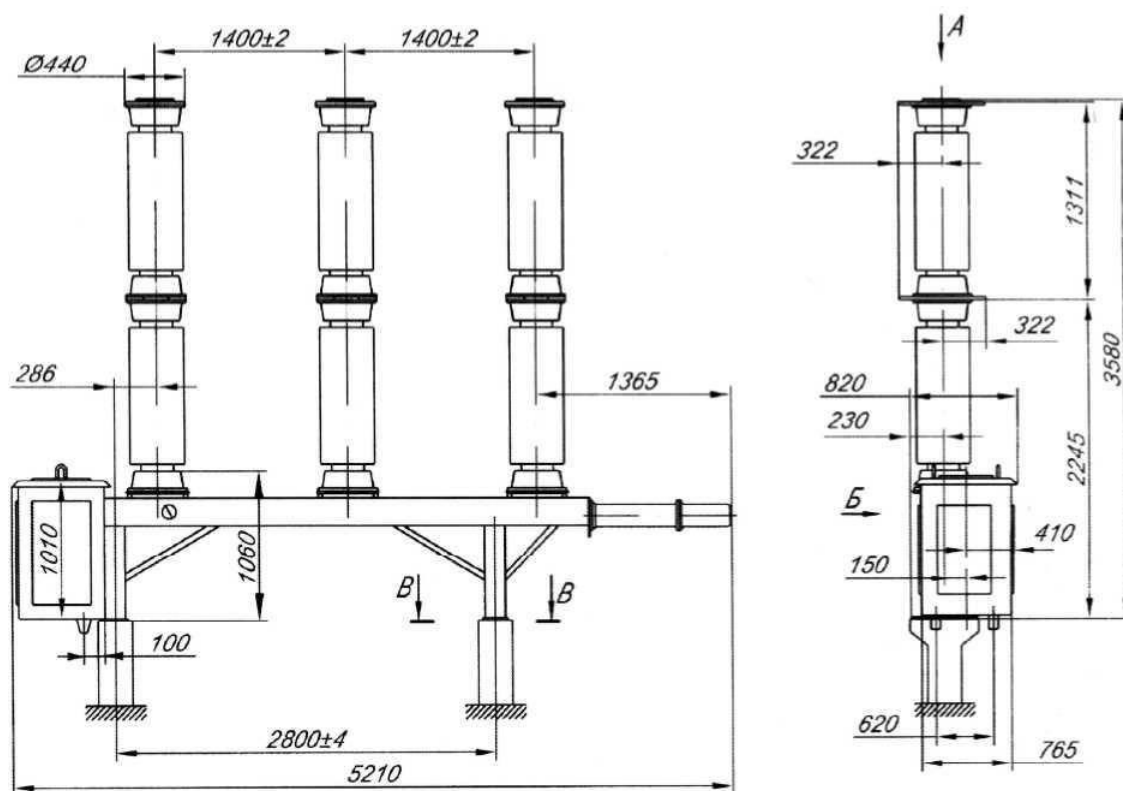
Габаритные, установочные и присоединительные размеры выключателя ВГТ-110II
